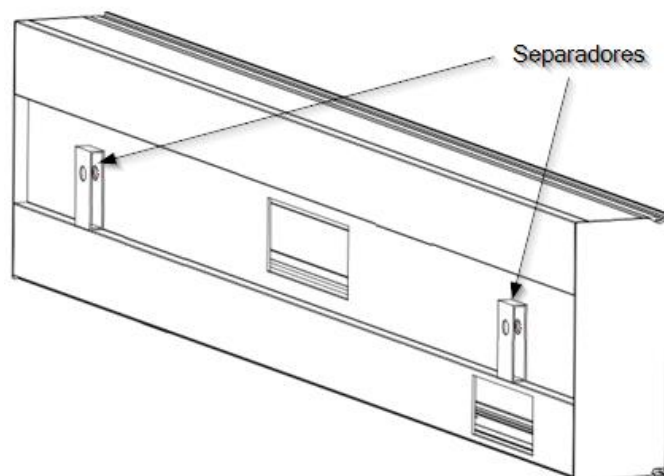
Separatoare spate pentru a evita îndoirea profilului central.
